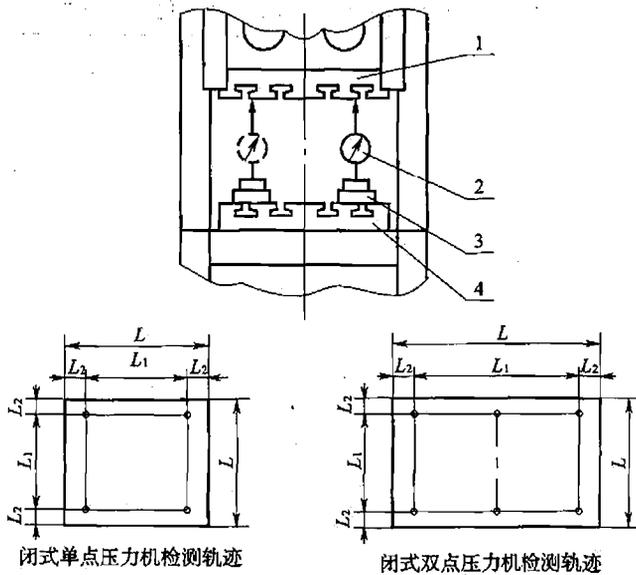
检验滑块下平面与工作台上平面的平行度
